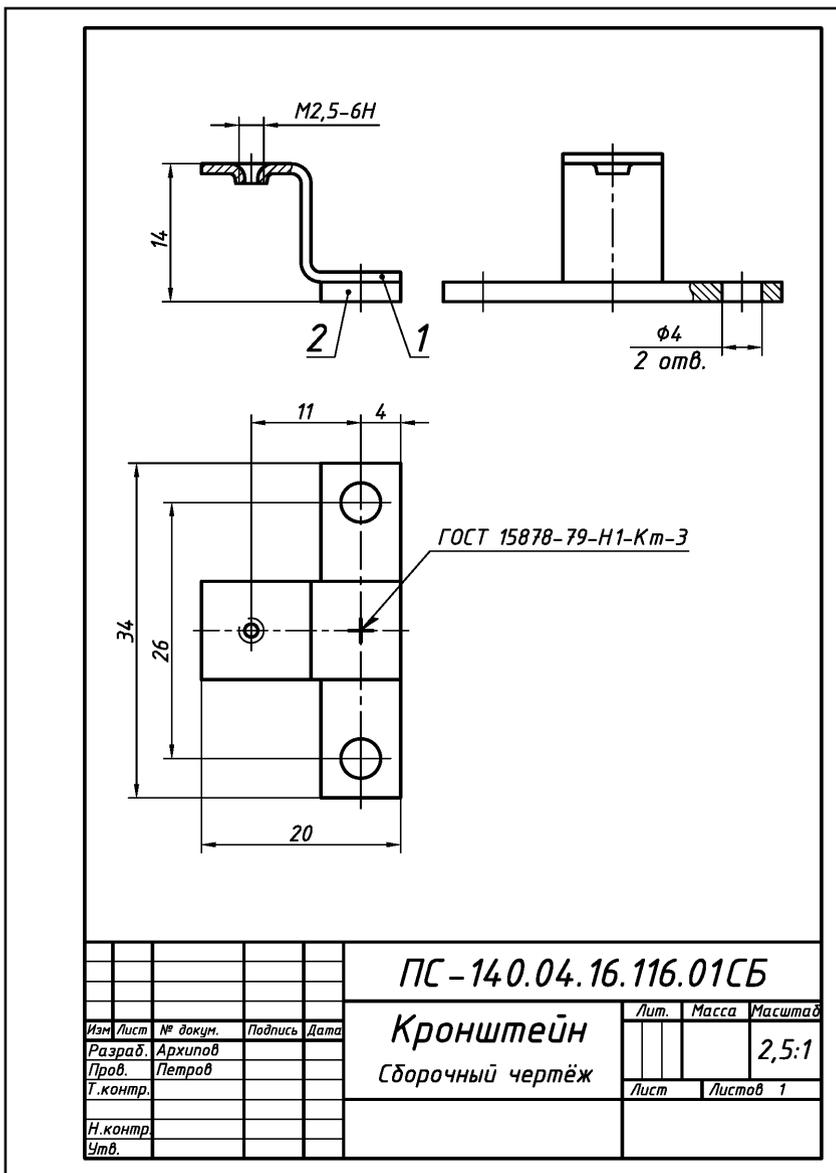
Оформление рабочего чертежа сборочной единицы «Кронштейн», образованной контактной точечной сваркой
